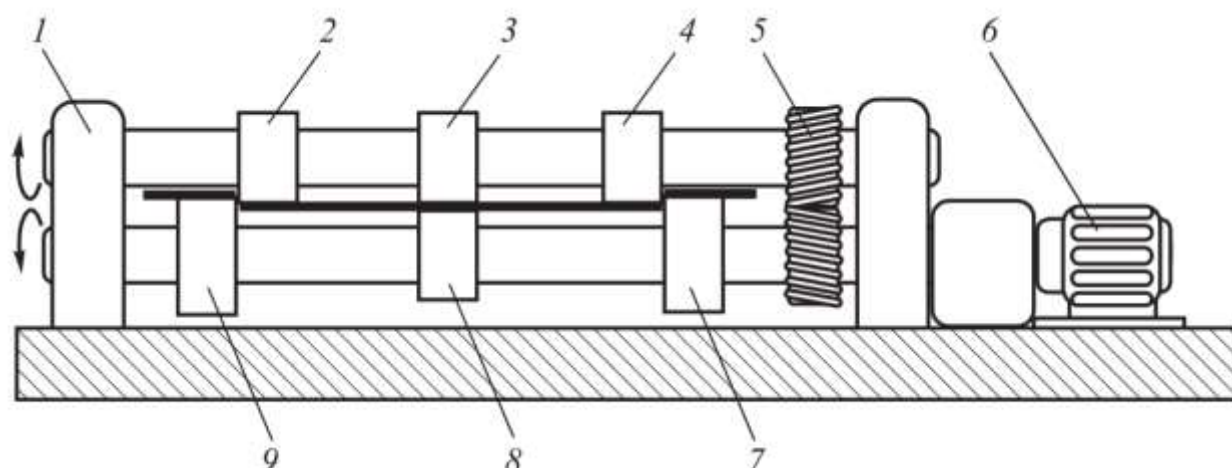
Схема дисковых ножиц для резки боковых кромок: 1 — станина; 2, 4, 7, 9 — режущие дисковые ножи; 3, 8 — опорные диски; 5 — шестерня; 6 — электропривод
